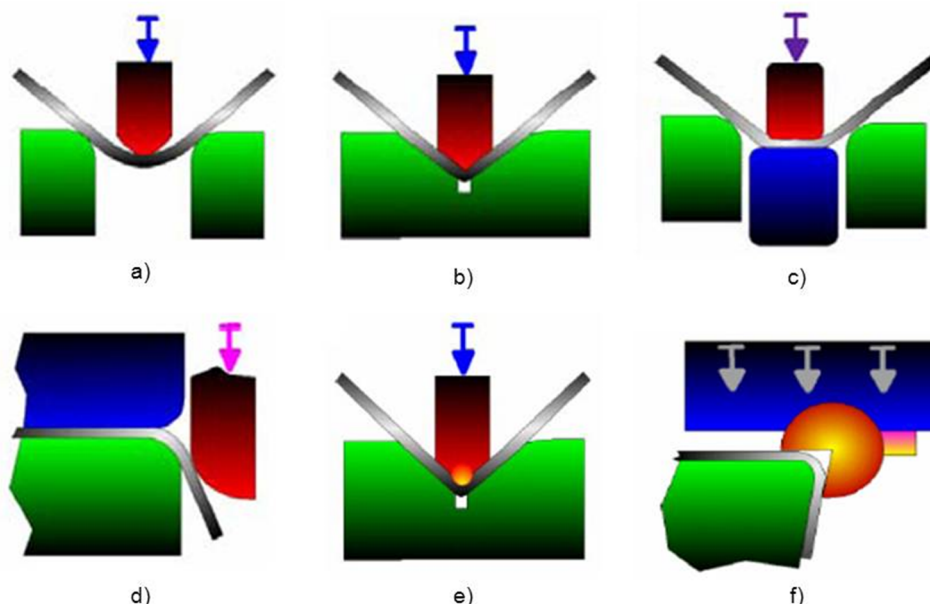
Tipos de quinagem, adaptado de [28] : a) Quinagem no ar; b) quinagem em “V”; c) quinagem em “U”; d) quinagem de flange com cunho de arraste; e) quinagem a fundo; f) quinagem rotativa
